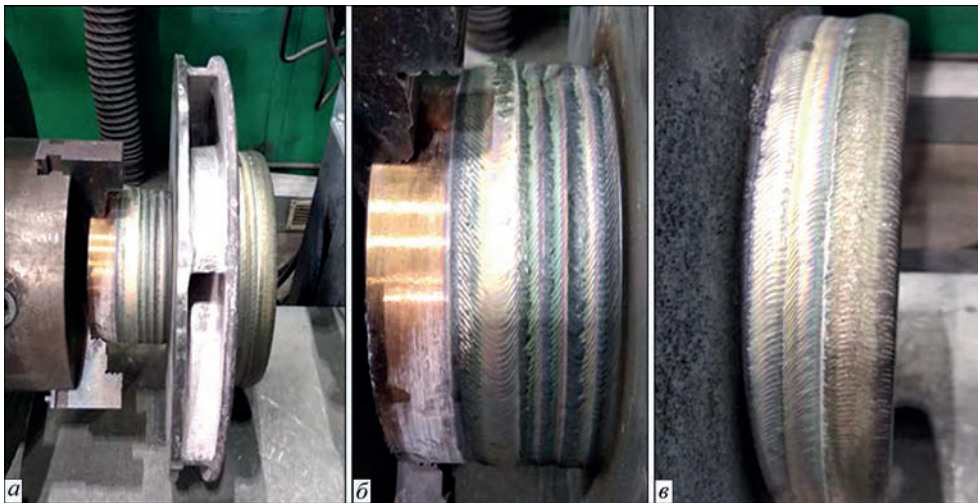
Плазмово-порошкове наплавлення робочого колеса насоса (а) та зовнішній вигляд напавленої поверхні на малому (б) та більшому (в) діаметрах робочого колеса
